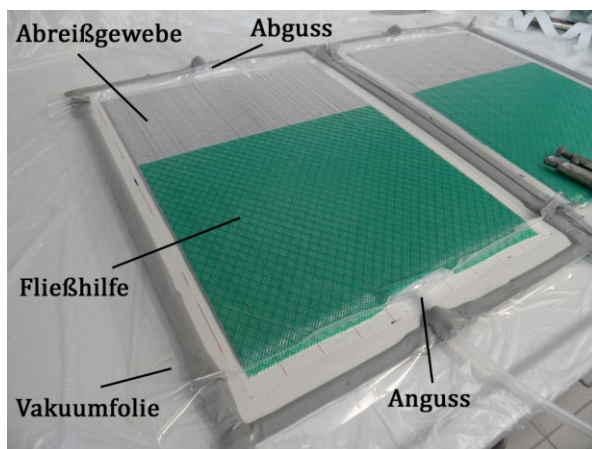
Abgedichtetes und unter Vakuum gesetztes Laminat vor der Harzinfusion
